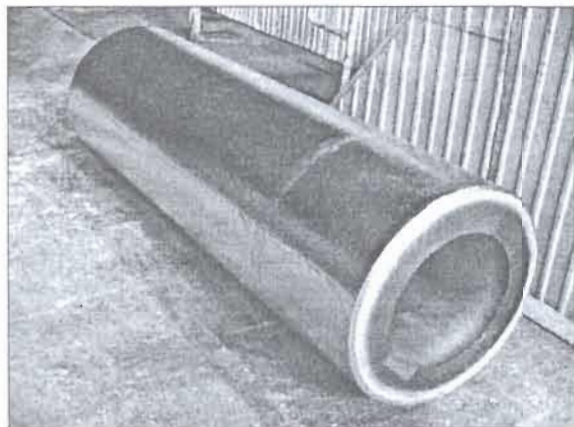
Трубная заготовка диаметром 600, высотой 400 и длиной 2000 мм
